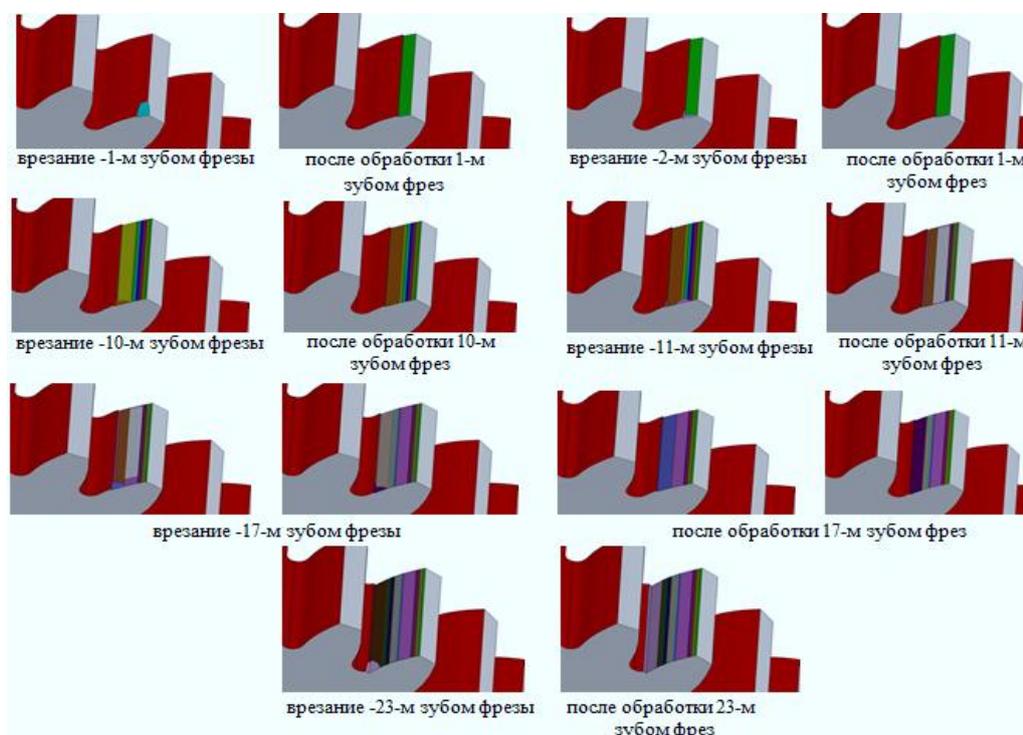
Процесс формирования шероховатости поверхностного слоя при последовательной обработке всех зубьев колеса червячной модульной фрезой
